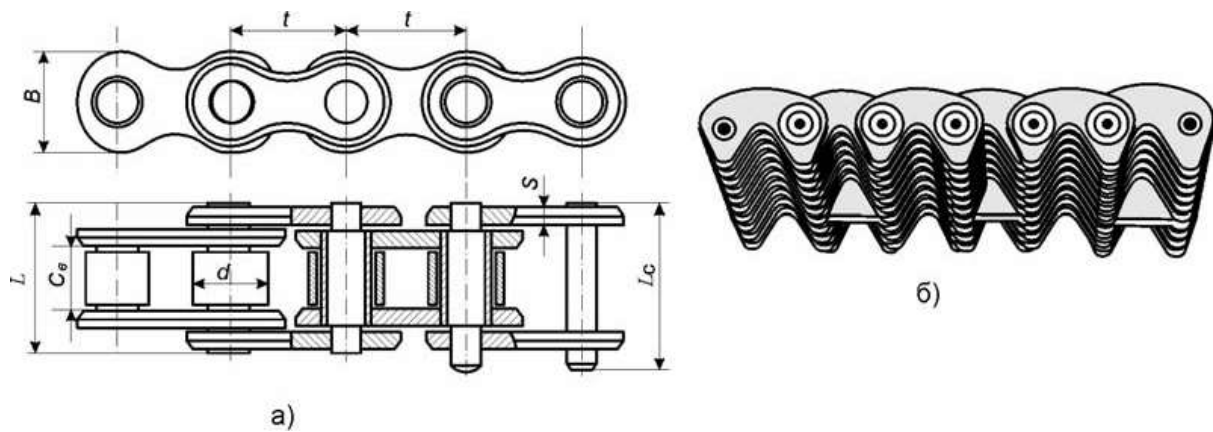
Приводные пластинчатые цепи: а — роликовые; б — зубчатые
